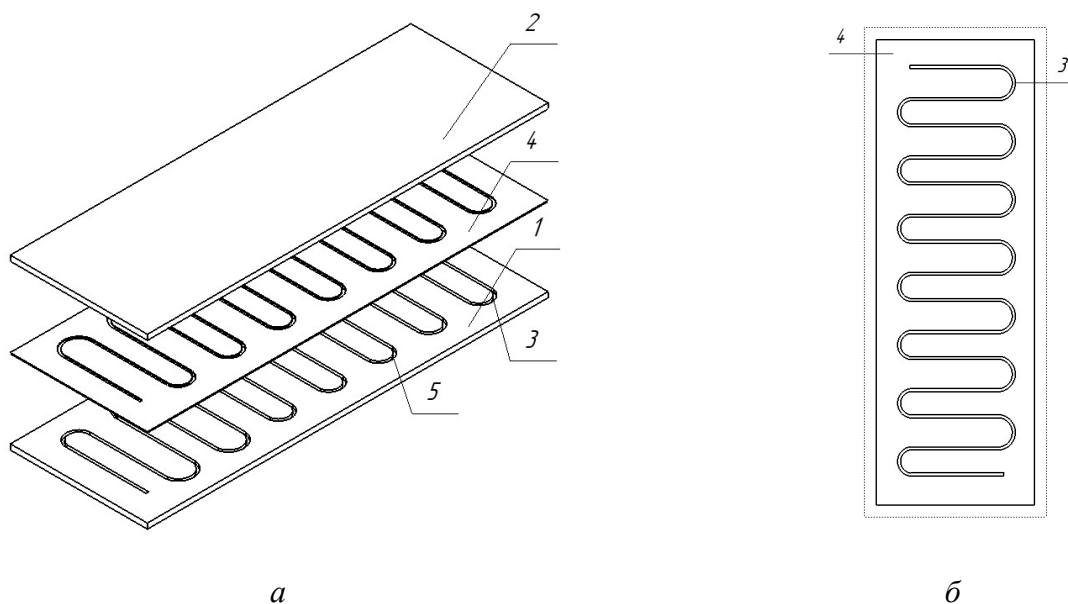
Экспериментальный образец: а – схемы конструкции микрофлюидной системы; б – промежуточный металлический слой (вид сверху)
